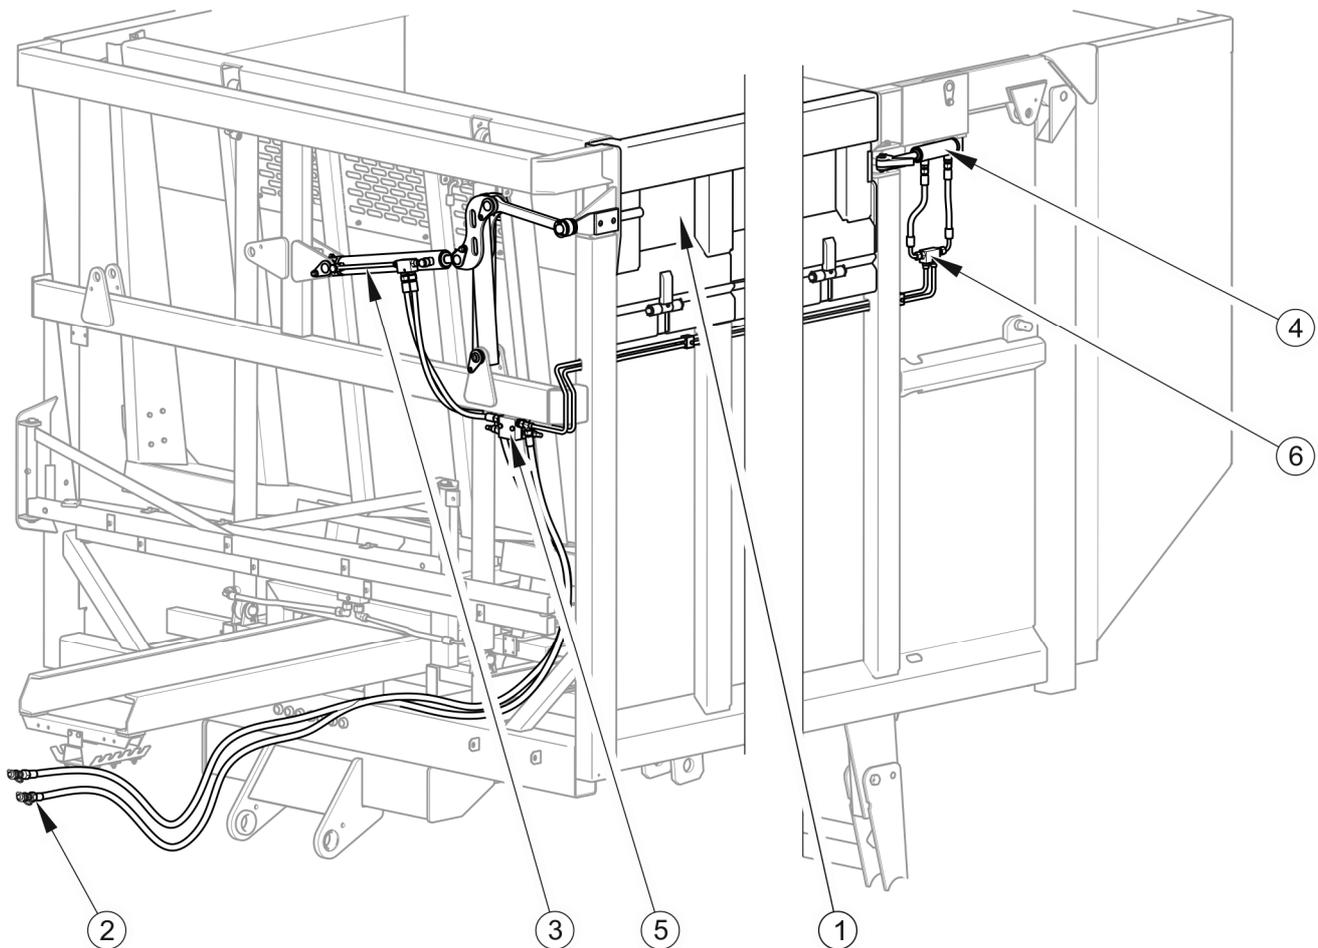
Schema dell'impianto sterzante idraulico
